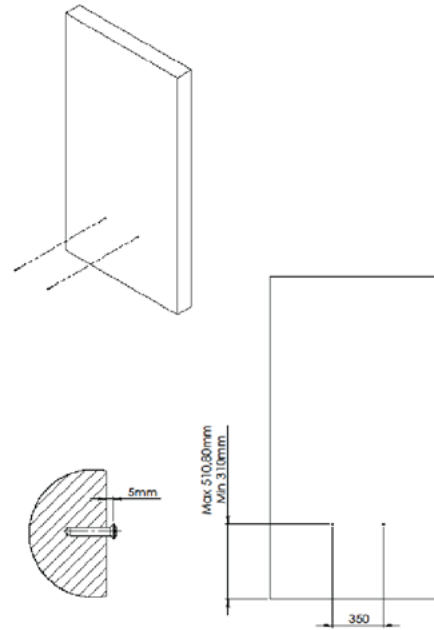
Einbau der Bolzen für die mittleren Befestigungslöcher
